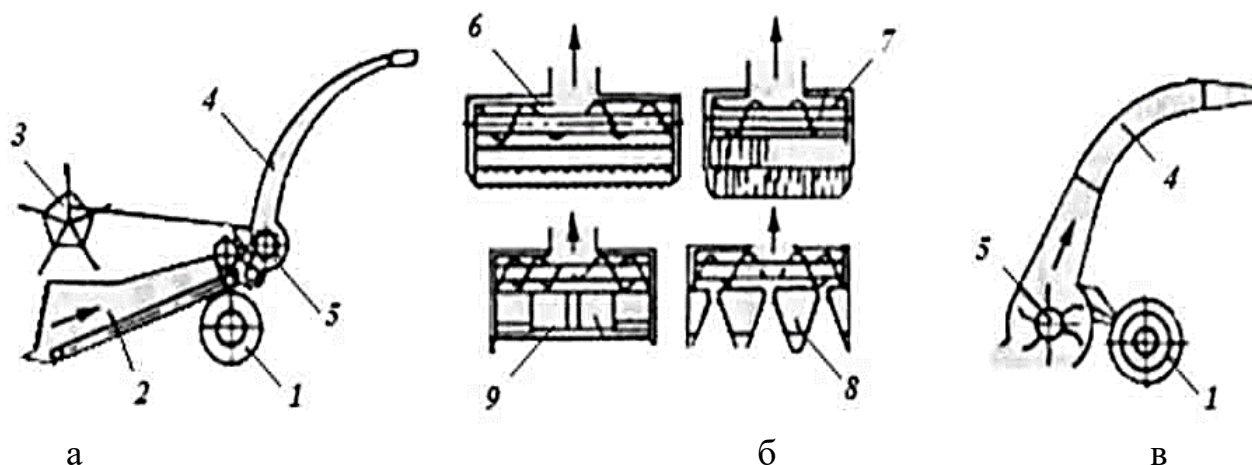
Схемы адаптеров кормоуборочных комбайнов: а – одноцелевых; б – универсальных; в – безжатвенных; 1 – ходовое колесо; 2 – платформа; 3 – мотовило; 4 – силосопровод; 5 – измельчающий аппарат; 6 – жатка для уборки трав; 7 – подборщик; 8 – ручьевая жатка для уборки кукурузы; 9 – жатка сплошного среза для уборки кукурузы
